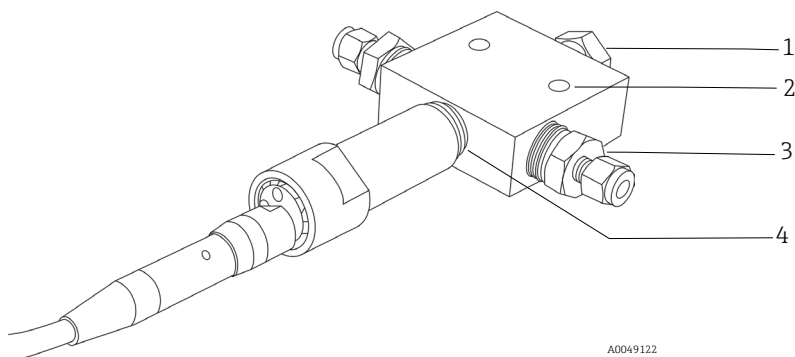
Зонд Rxn-30, встроенный в крестообразный фитинг NPT ½ дюйма
